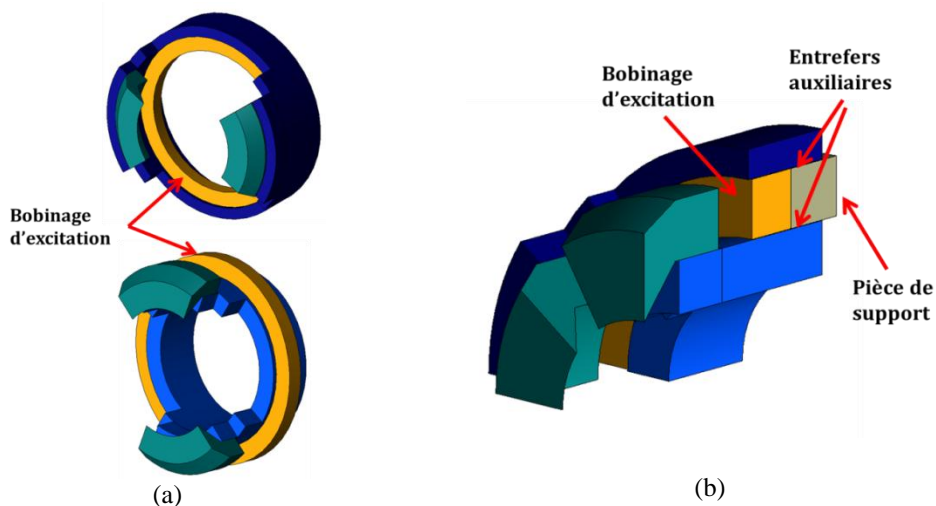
(a) Vue du bobinage du rotor et (b) vue de la fermeture du circuit magnétique du rotor
